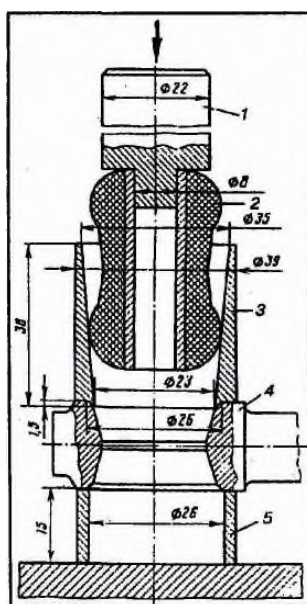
Запрессовка внутреннего резинометаллического шарнира рулевой тяги автомобиля ЗАЗ-1102 с помощью приспособления:
